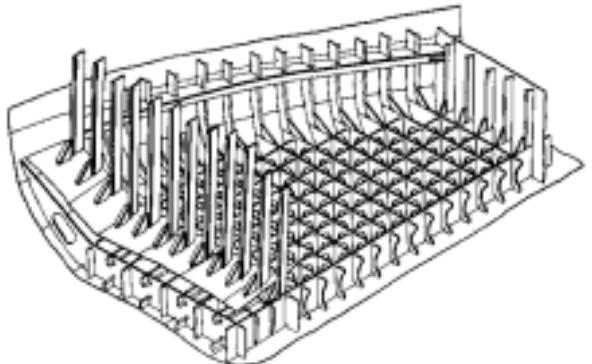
Поперечная система двойного перекрытия в трюме рулевого (наснит второго дна и обшивка поперечной спарбции не показаны)
